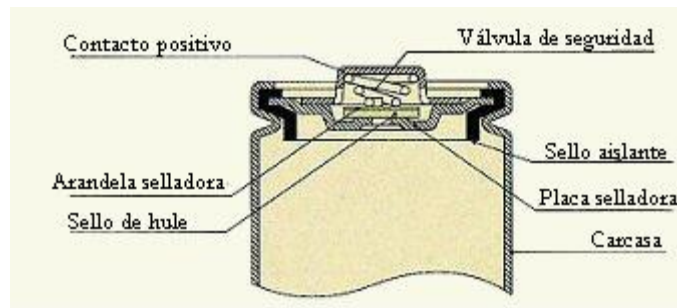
Estructura de las baterías de la parte superior de las baterías Ni-Cd.
